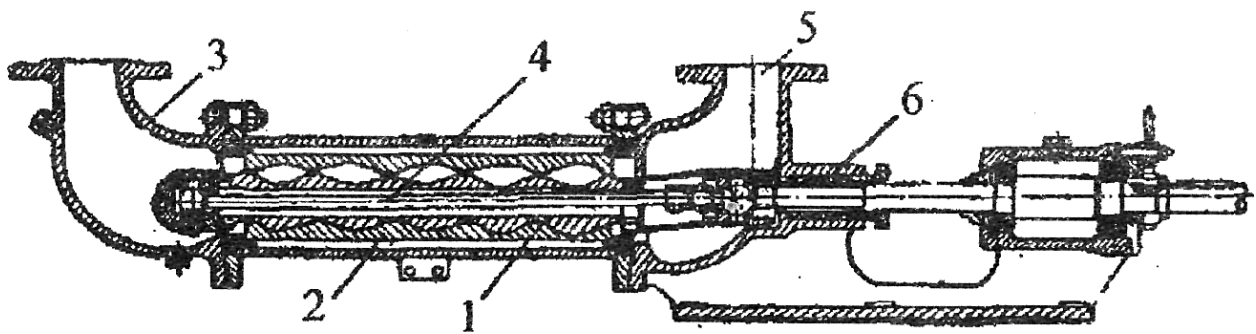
Гвинтовий насос: 1 – ротор; 2 – статор; 3 – напірний патрубок; 4 – вал; 5 – всмоктувальний патрубок; 6 – сальник
